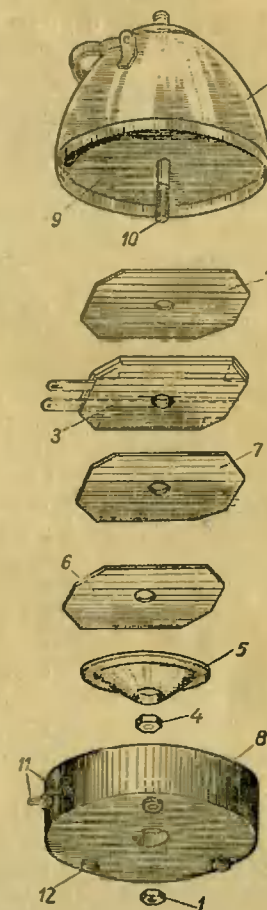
Электрический чайник в разобранном виде: 1 — нижняя скрепляющая гайка, 2 — корпус чайника, 3 — нагревательный элемент, 4 — вжимная гайка, 5 — металлический диск для соединения деталей, 6 — металлическая пластина, 7 — асбестовые изолирующие прокладки, 8 — основание чайника, 9 — дно чайника, 10 — соединительный болт, 11 — выводные контакты, 12 — изоляционные подкладки — ножки.
